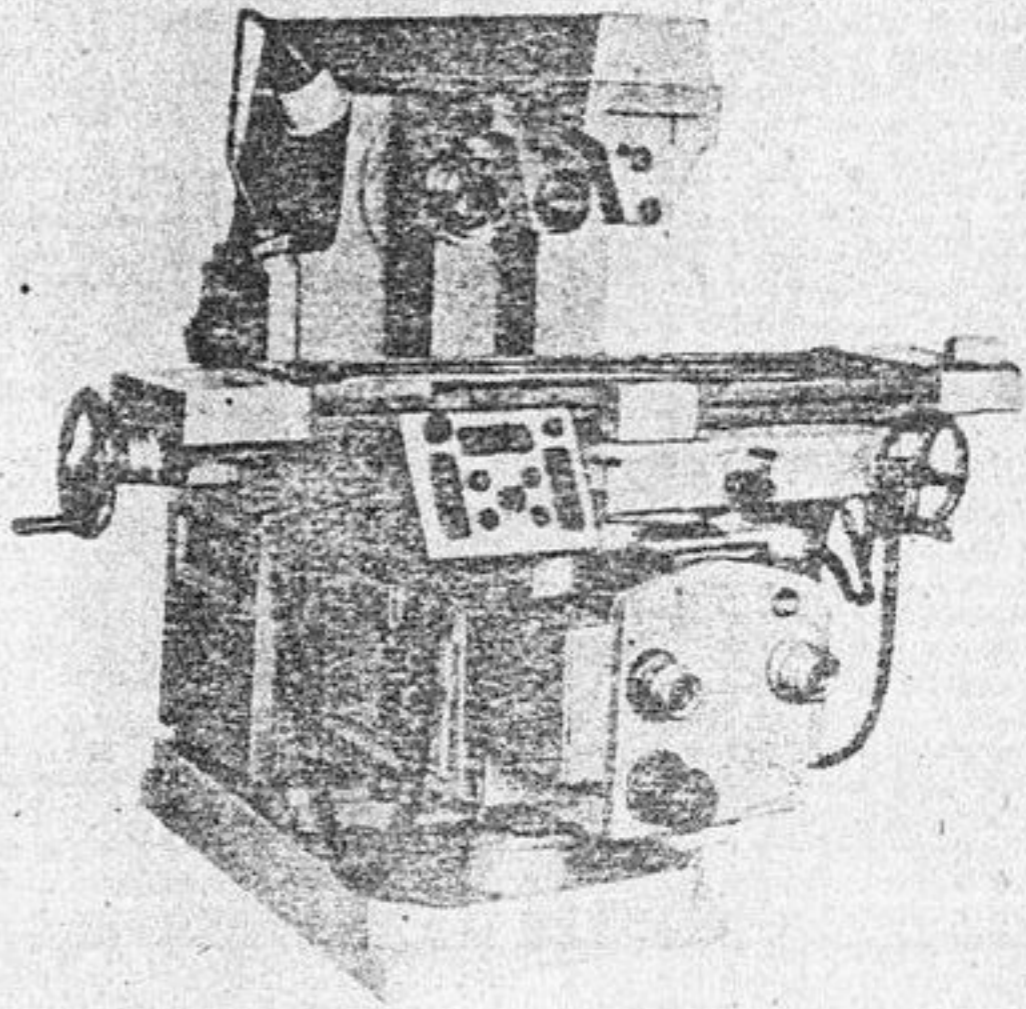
Универсальный консольно-фрезерный станок 6Т82-29
